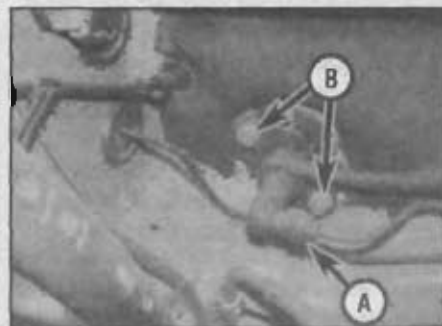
Расположение гайки (А) крепления трубопровода и болтов (В) крепления главного цилиндра сцепления
